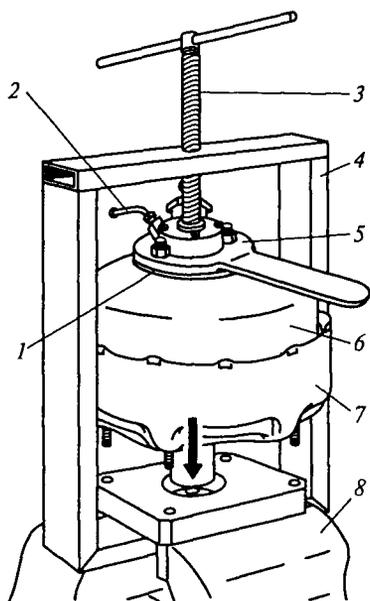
Приспособление для разборки и сборки вакуумного усилителя:
